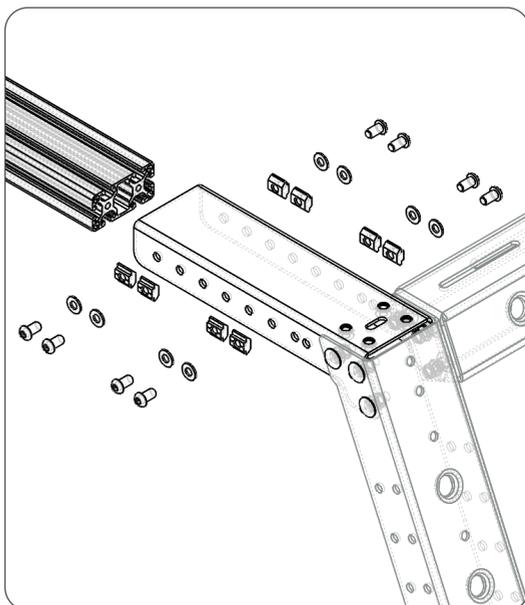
Detailansicht der verschraubten Dachstrebe / detailed view of bolted down roof strut
